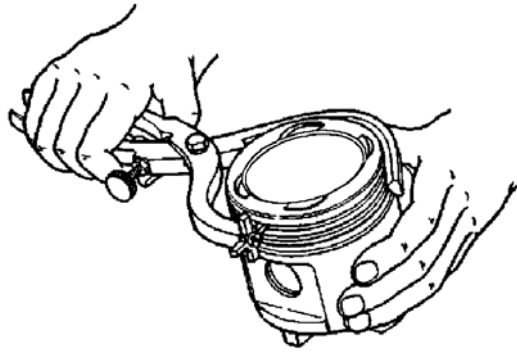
Очистка нагара в канавках поршней с помощью приспособления
